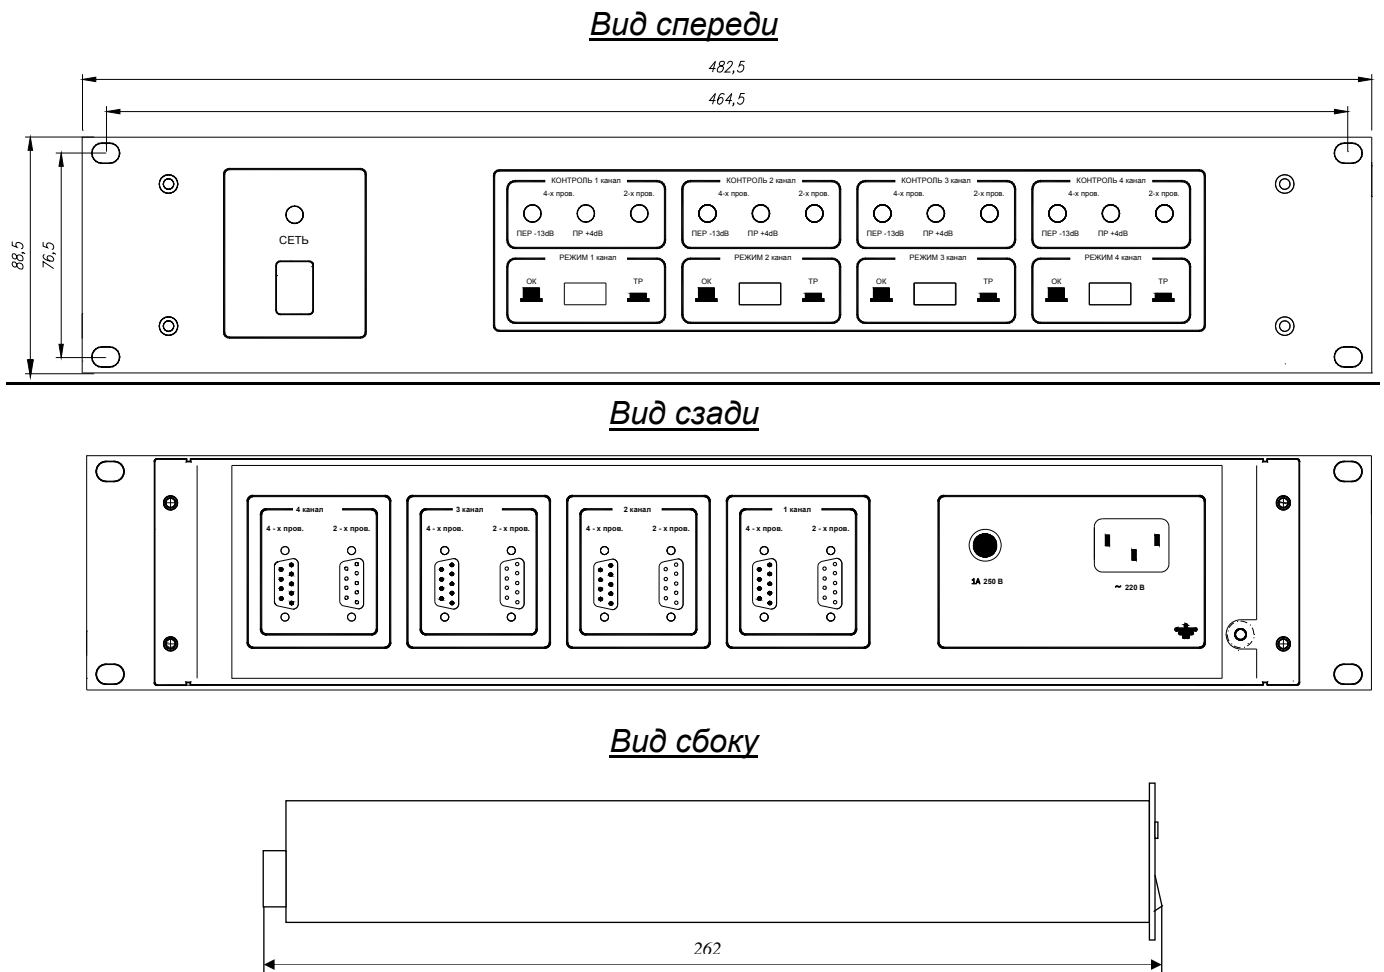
Внешний вид и габаритные размеры изделия ДСВ-4
